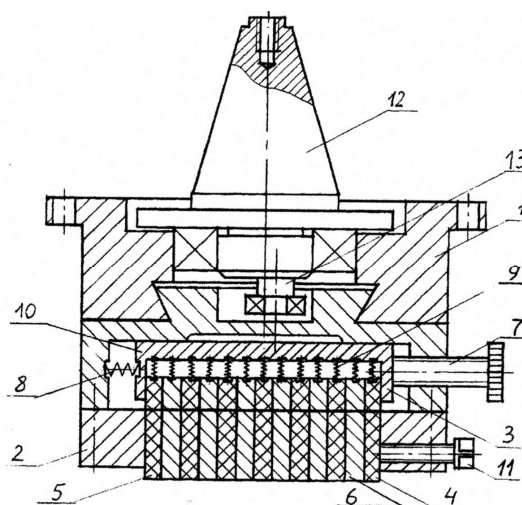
Устройство для магнитно-абразивной обработки патент RU №2220836
